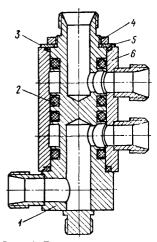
Поворотные соединения: 1 — основание; 2 — кольцо; 3 — сальник; 4 — круглая гайка; 5 — шайба; 6 — корпус
